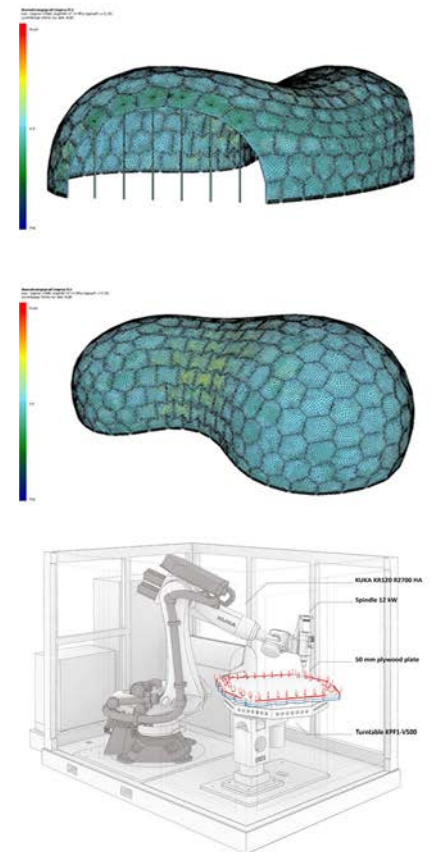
Halle d'exposition du Landesgartenschau. Enveloppe structurale conçue et fabriquée numériquement. D'après ICD/ITKE de Stuttgart.
